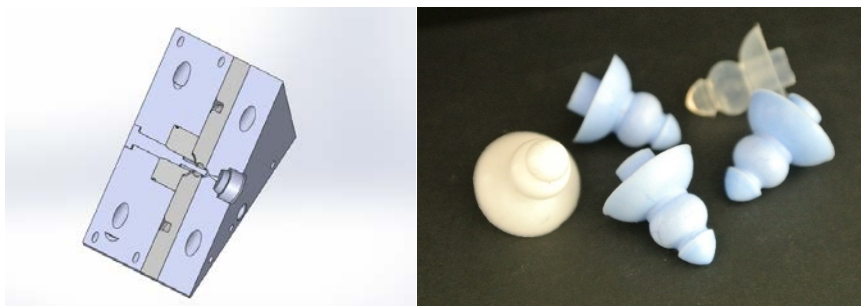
Werkzeug (links) und Bauteile (rechts) aus geschäumtem Flüssigsilikonkautschuk
